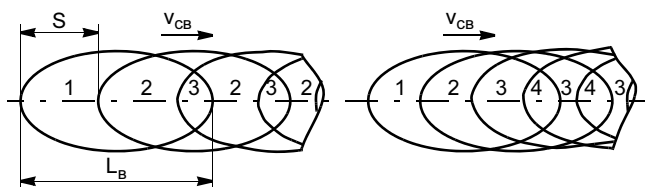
Схема перекрытия сварных точек для различных скоростей сварки при импульсно-дуговом процессе
